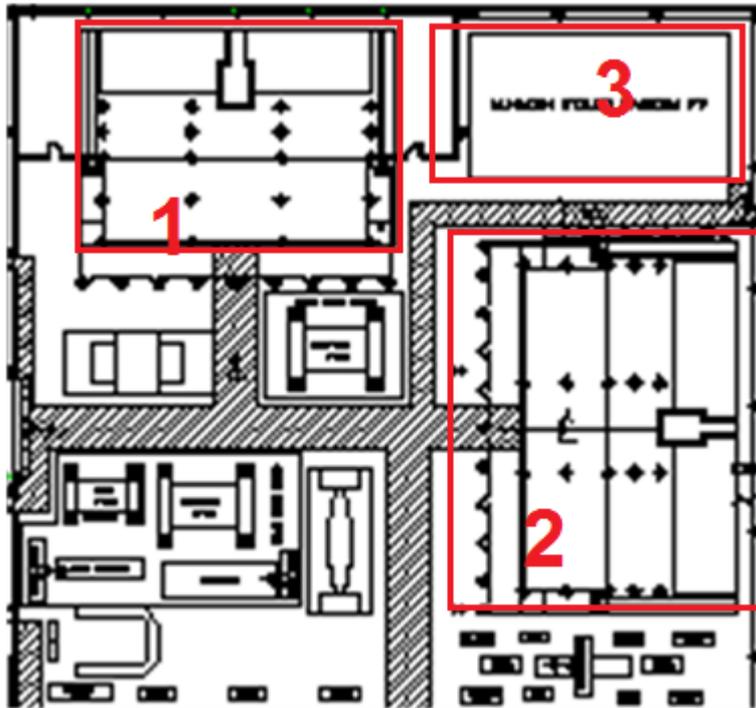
Zona de almacenamiento de útiles de laminado automático.
